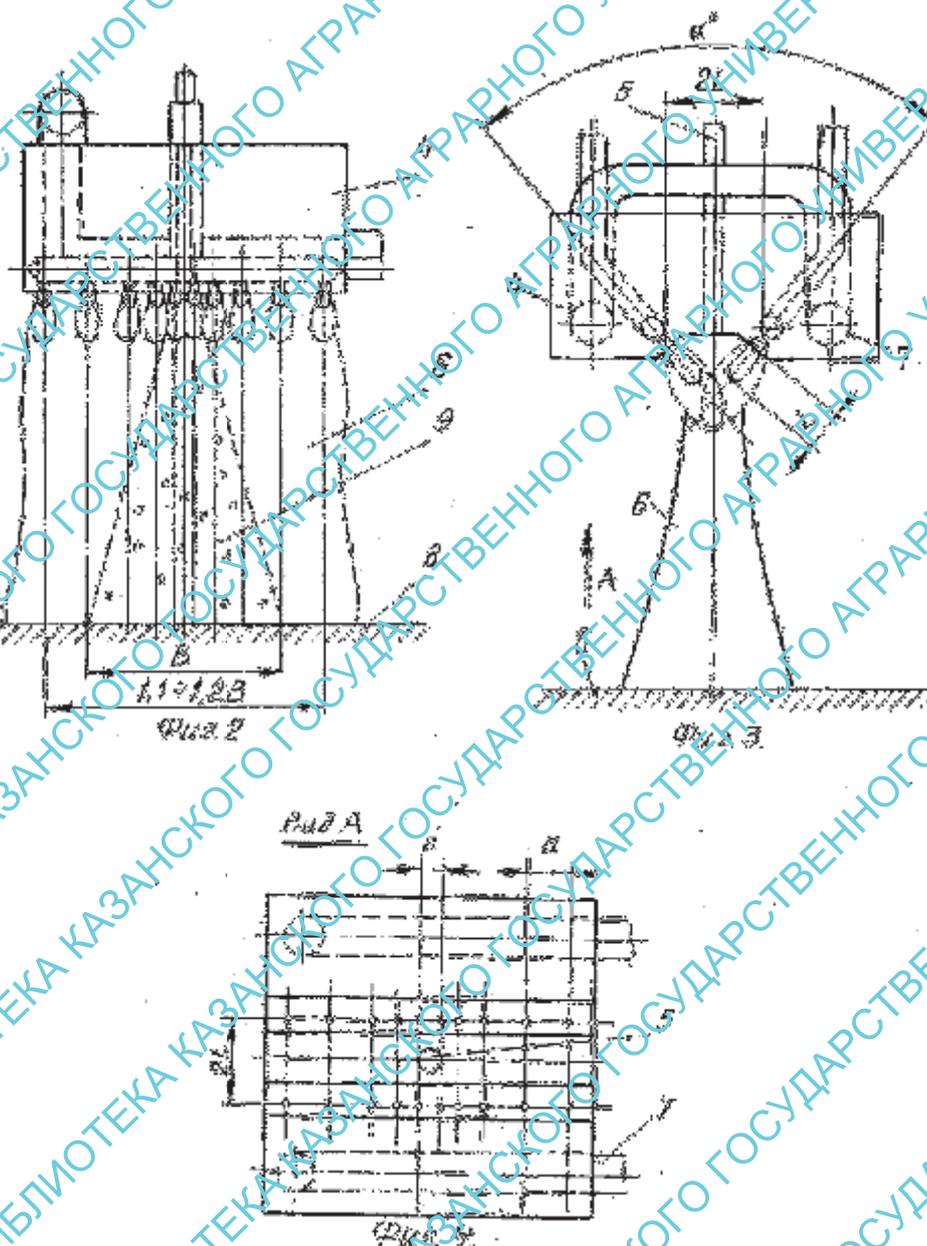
Горелка для газопламенного напыления покрытий из тугоплавких порошков.
